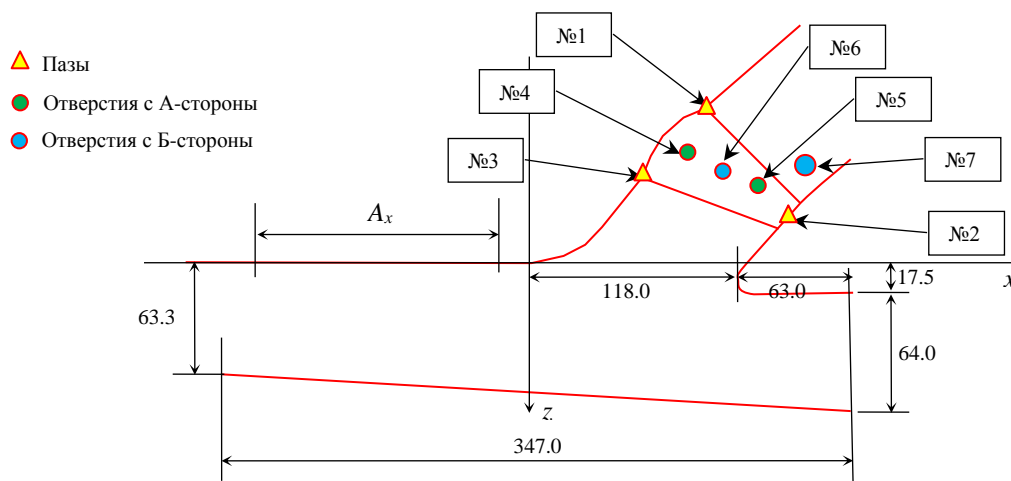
Эскиз испытательного образца с характерными размерами и местами расположения отражателей
